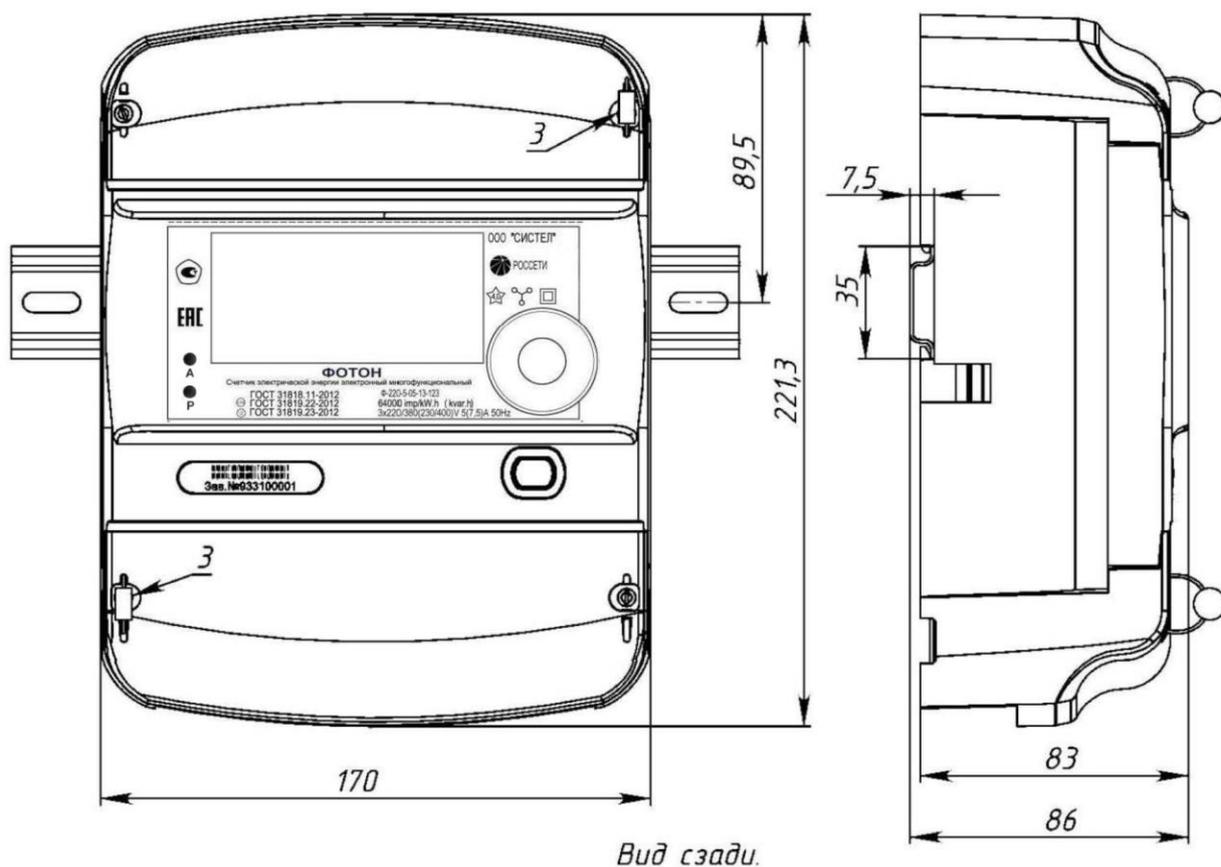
Габаритные и установочные размеры счетчика «Фотон» в пластмассовом корпусе
